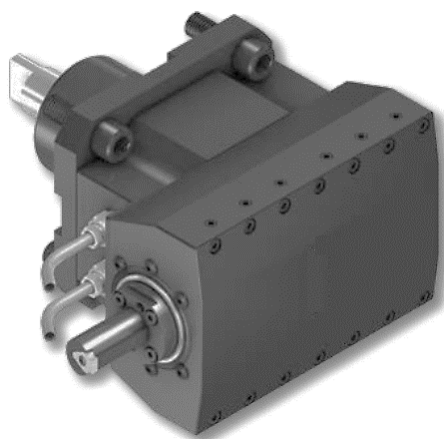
Общий вид приводного долбежного блока для токарного станка с ЧПУ
